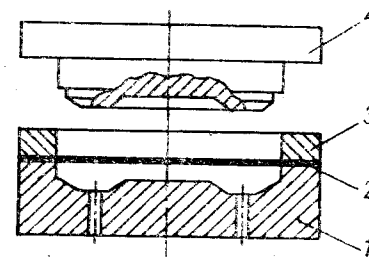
Схема штапування заготовок з листових пластмас:
